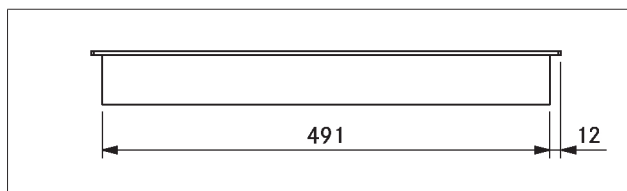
CKI apparatets dimensjoner sett fra siden
